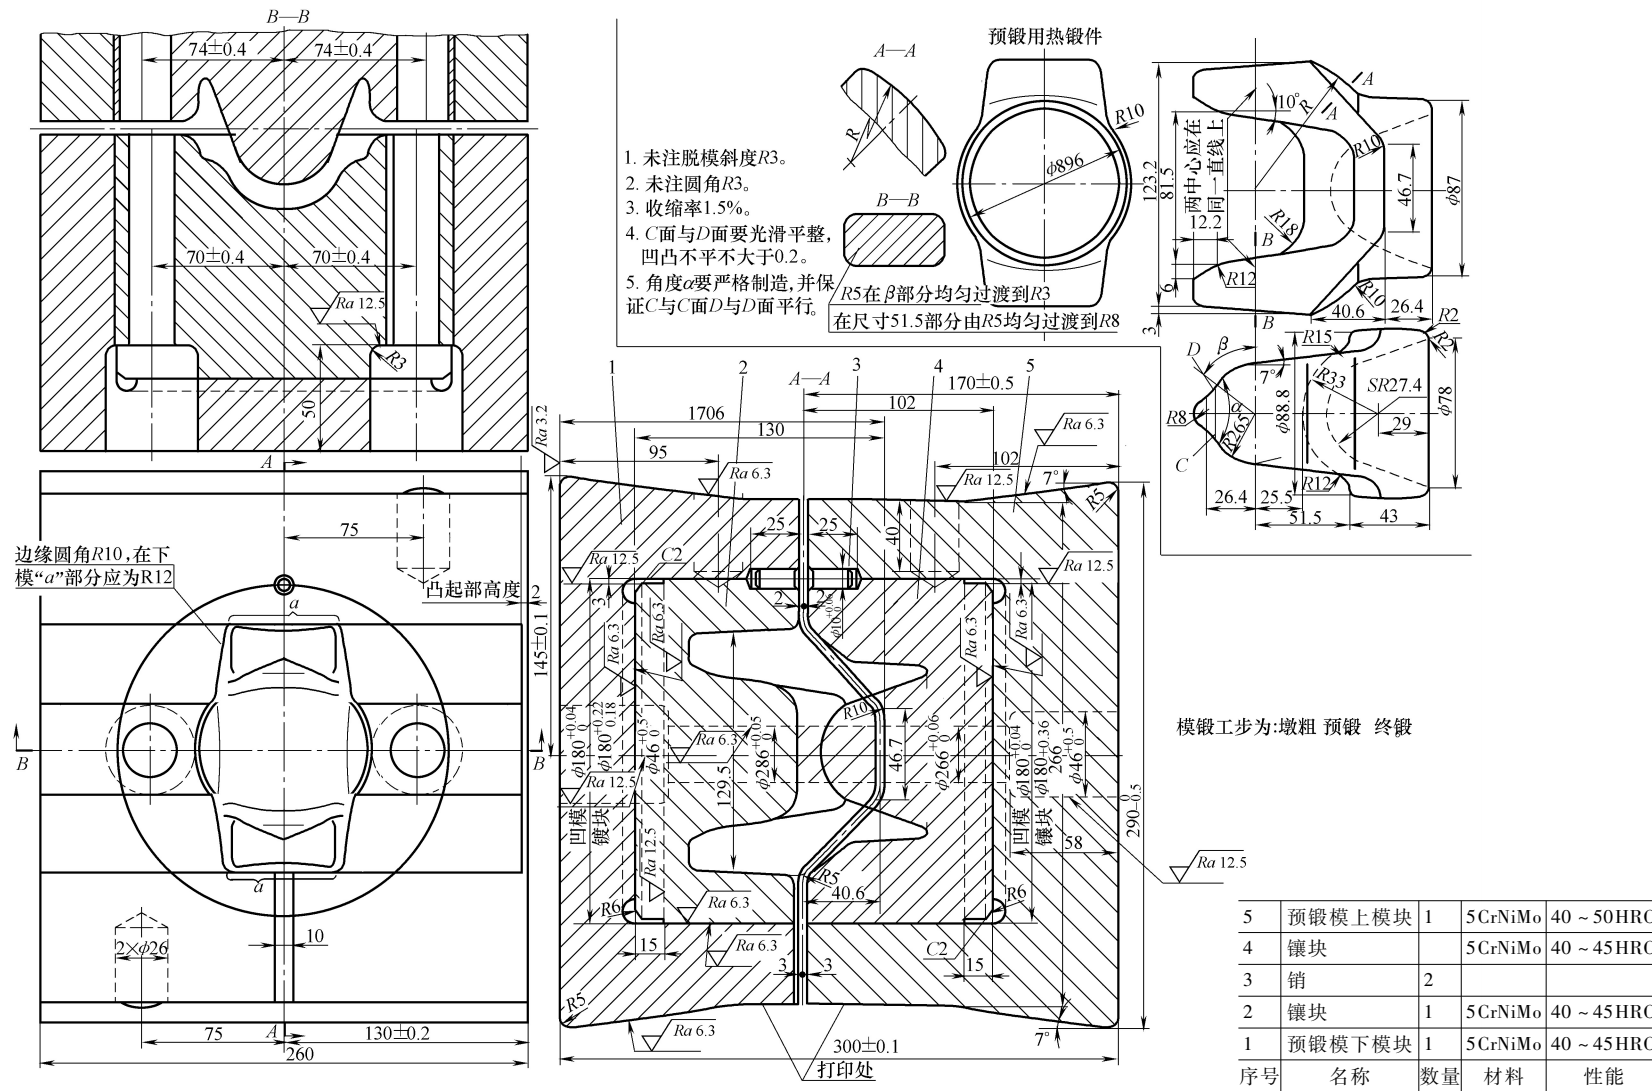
万向节叉预锻热锻件及预锻模 (16000kN)
